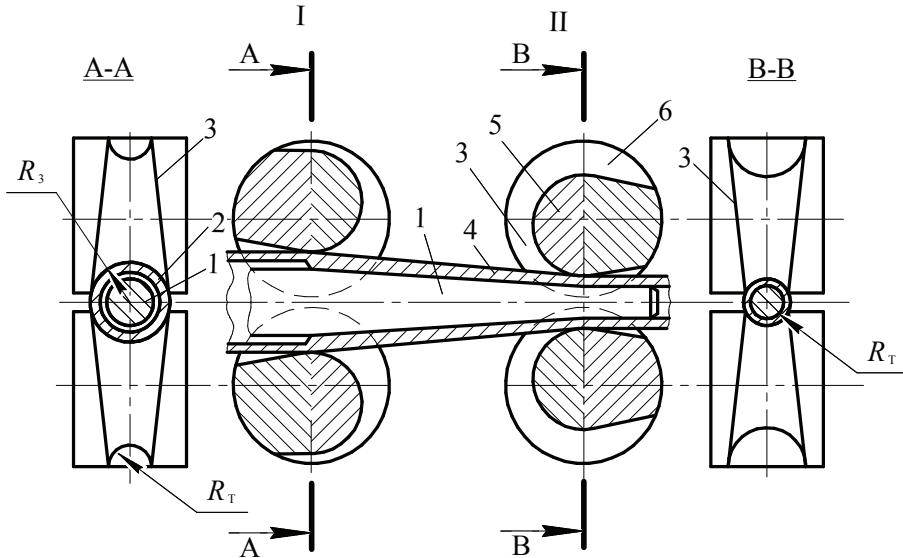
Схема прокатки труб на стане ХПТ [27, с. 449]:
